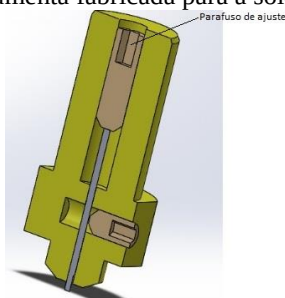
(A) – Desenho esquemático da ferramenta utilizada na soldagem FSW. Fonte: os autores, 2016.
